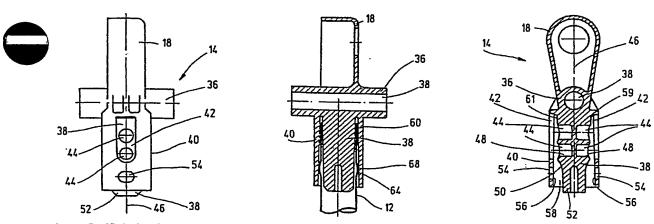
Wischerlager mit Hohlprofil- Querschnitt am Crimpzapfen (EM 01/1211; R304406, Stand der Technik)
